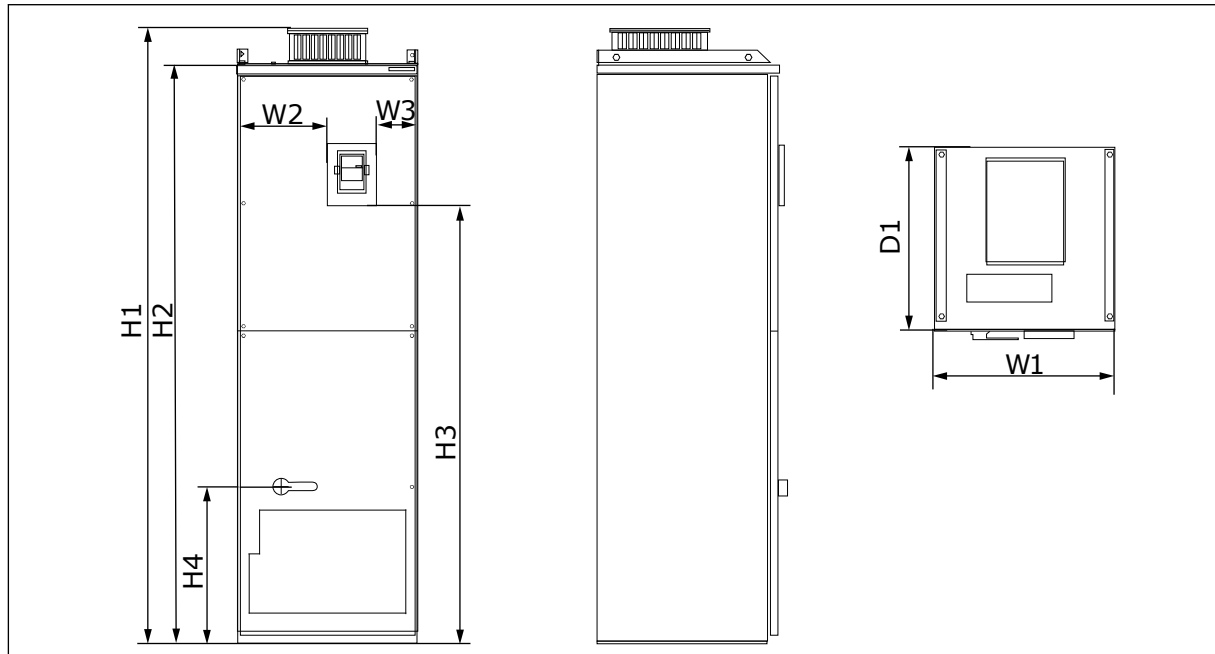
Dimensioni dell'inverter NXS e NXP, FR10 e FR11
